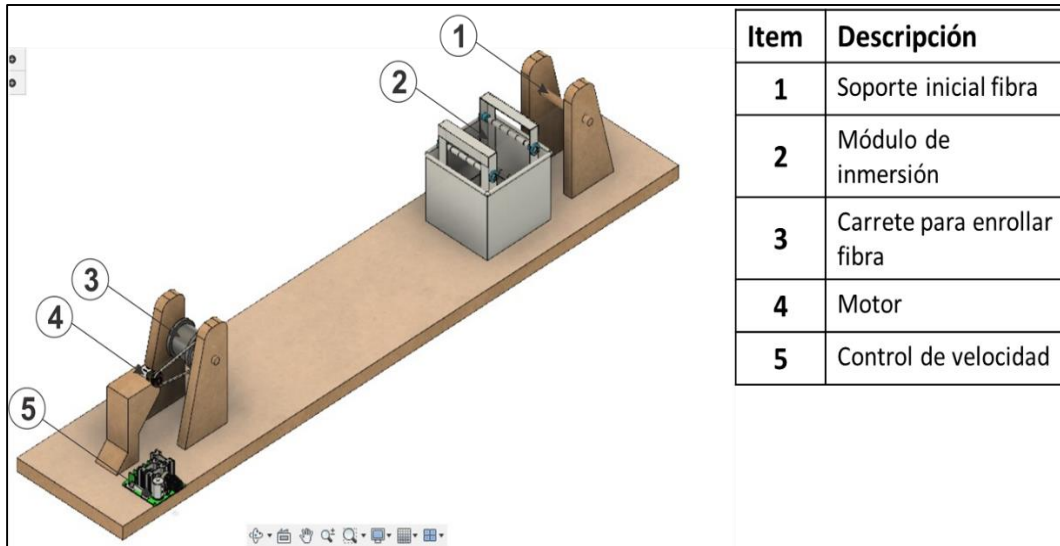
Diseño de sistema para realizar la técnica de inmersión. Fuente: propia.
